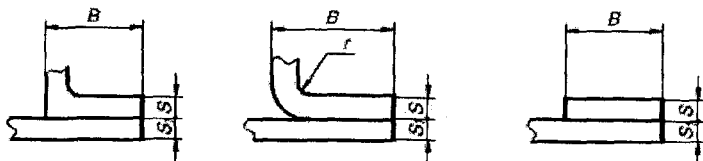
Виды нахлестки сварных соединений, выполняемых контактной точечно рельефной и шовной сваркой
